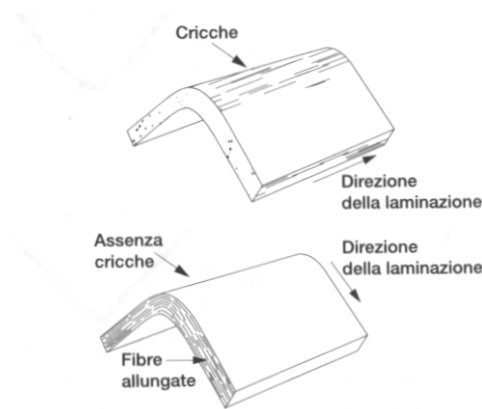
Effetto della direzione di laminazione sulla piegatura.
